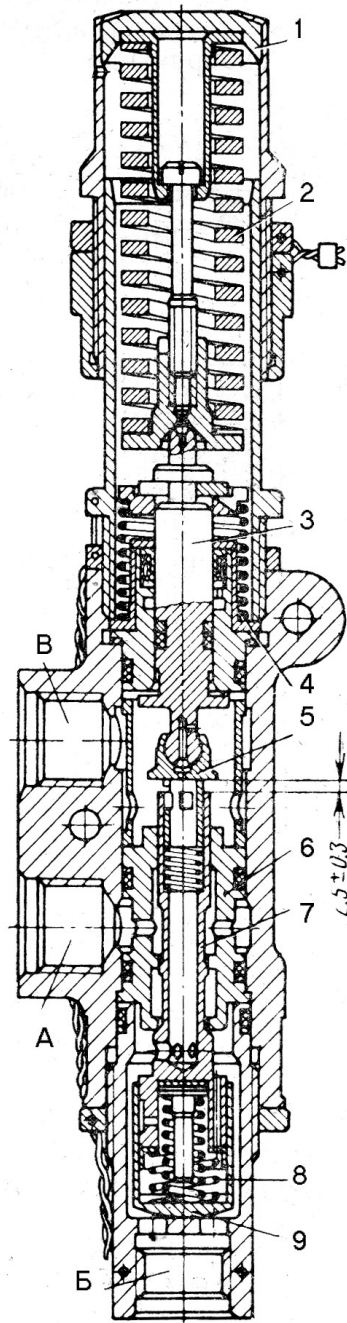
Конструкція гідравлічного редукційного клапана прямої дії:
